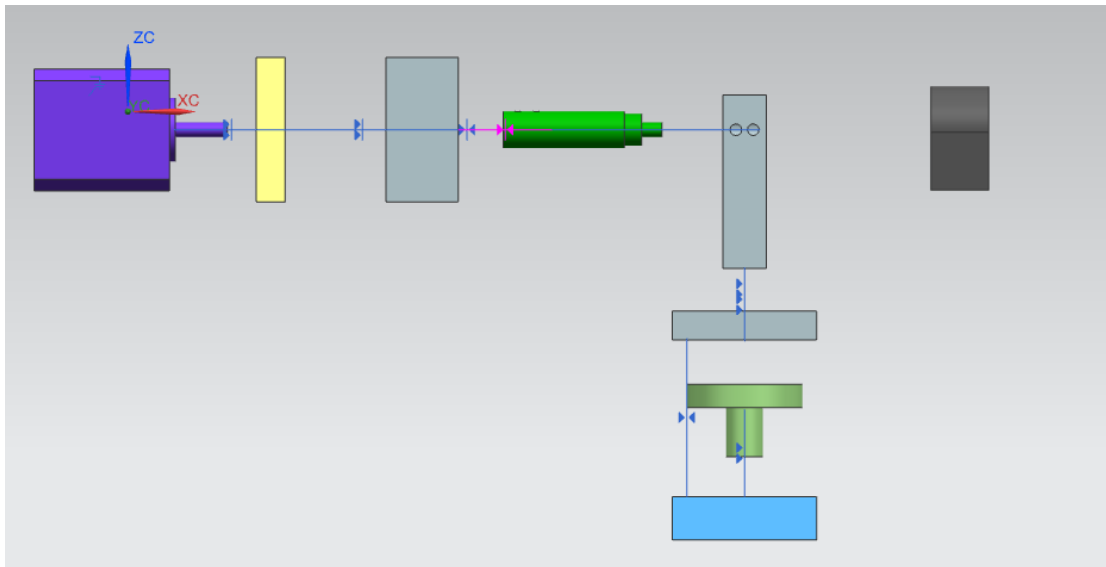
Diseño 3. Ensamble vista frontal explosiva.
